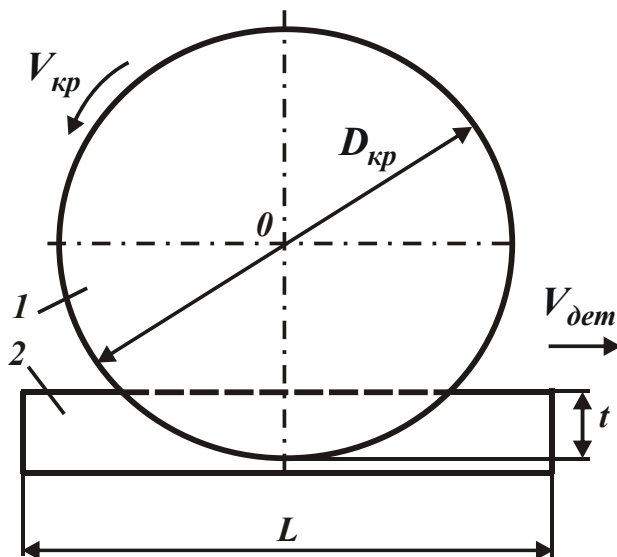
Расчетная схема шероховатости на боковой поверхности зуба колеса при шлифовании торцом круга: 1 – круг; 2 – зуб колеса
